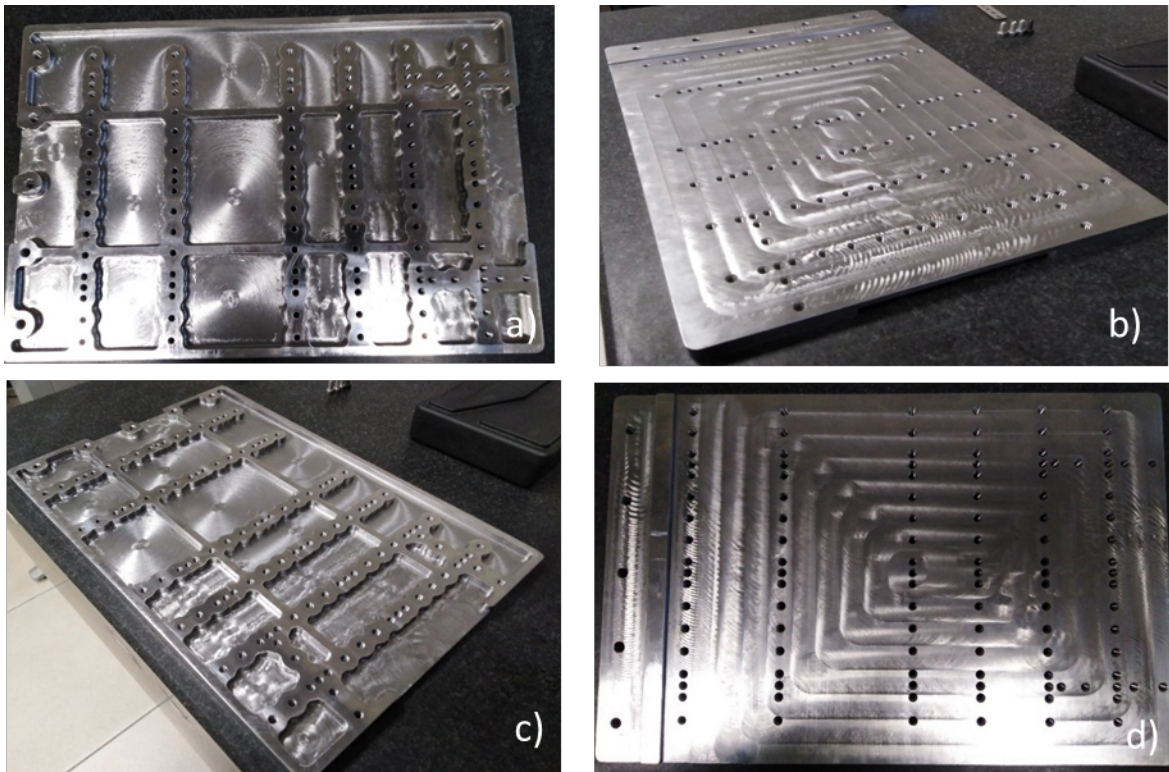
Placa Base A4041. a) Cara inferior, b) cara superior c) vista isométrica, d) vista superior.
